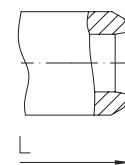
с резьбовым соединением под приварку и приварной насадкой (только PN16)
